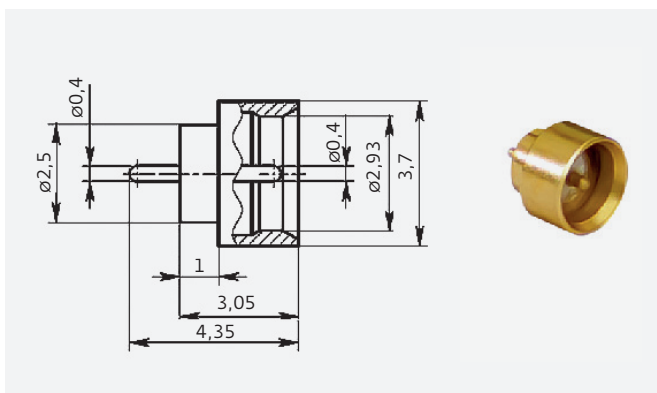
Герметичная приборная вилка КРПГ.433434.054 (АО "НПП "Исток")
